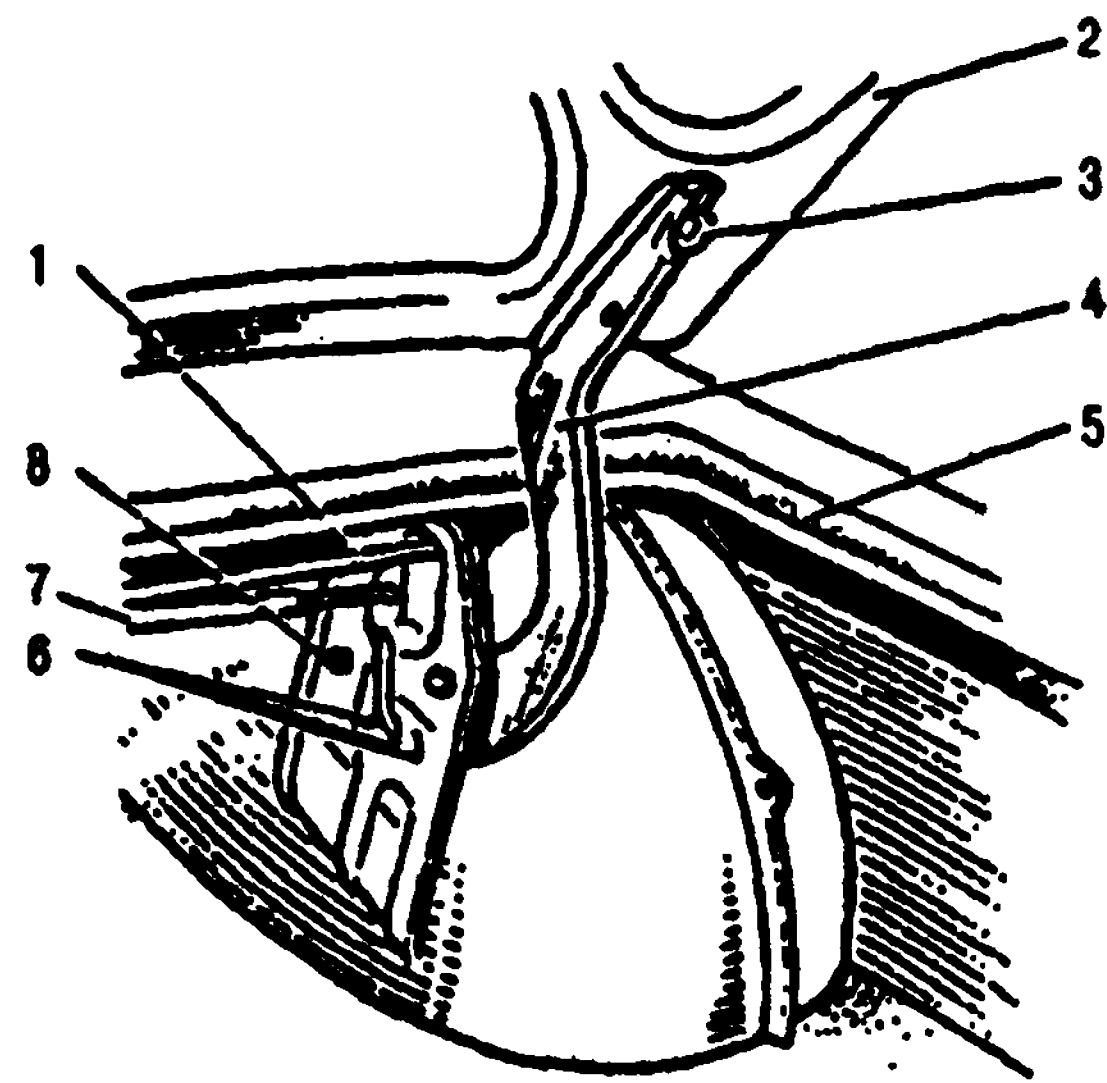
Крышка багажника: 1 - торсион; 2 - крышка; 3 - болт; 4 - петля; 5 - уплотнитель; 6 - регулировочные отверстия; 7 - защитная трубка; 8 - болт крепления петли к корпусу
